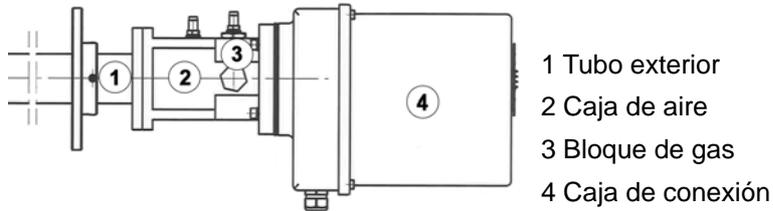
Componentes principales del quemador de ignición LAMTEC GFI
